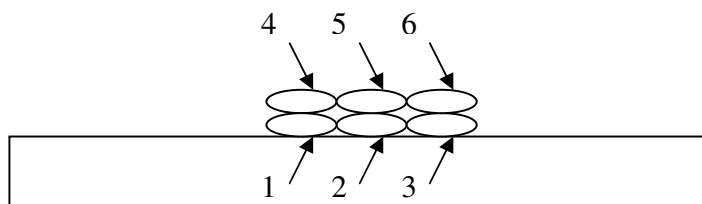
Esquema da sequência de execução e localização dos passes de soldadura
